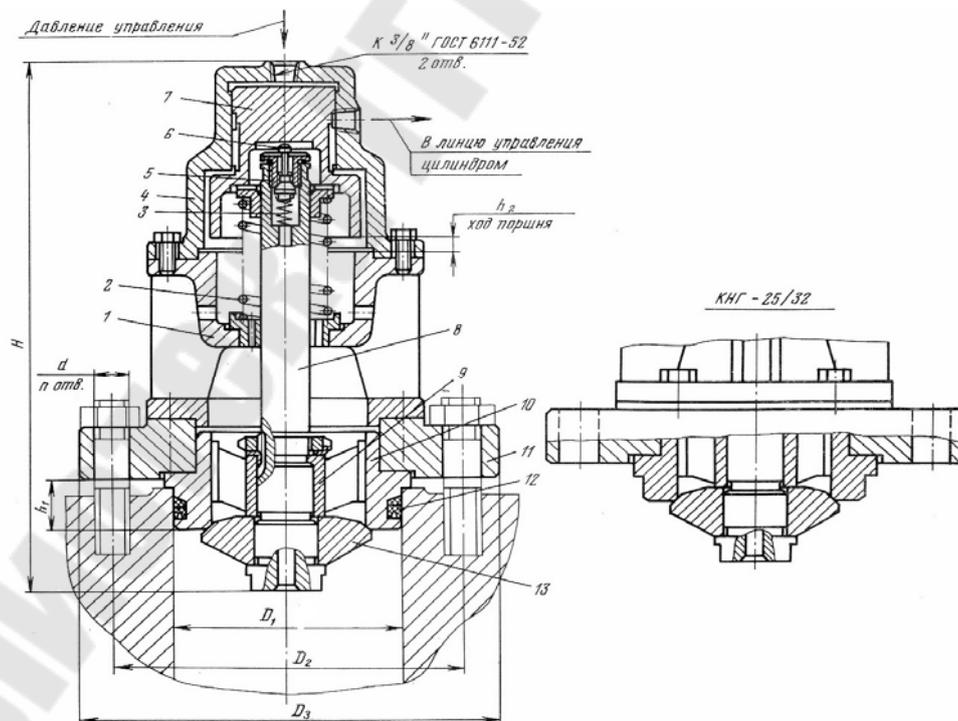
Конструкция, габаритные и присоединительные размеры клапана наполнения
